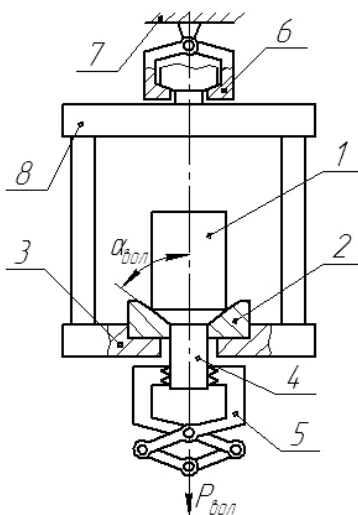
Схема и устройство волочения прутка: 1 – заготовка; 2 – волока; 3 – волокодержатель; 4 – "захватка"; 5 – клещи; 6 – центрирующая опора; 7 – станина испытательной машины; 8 – жесткая рамка устройства
